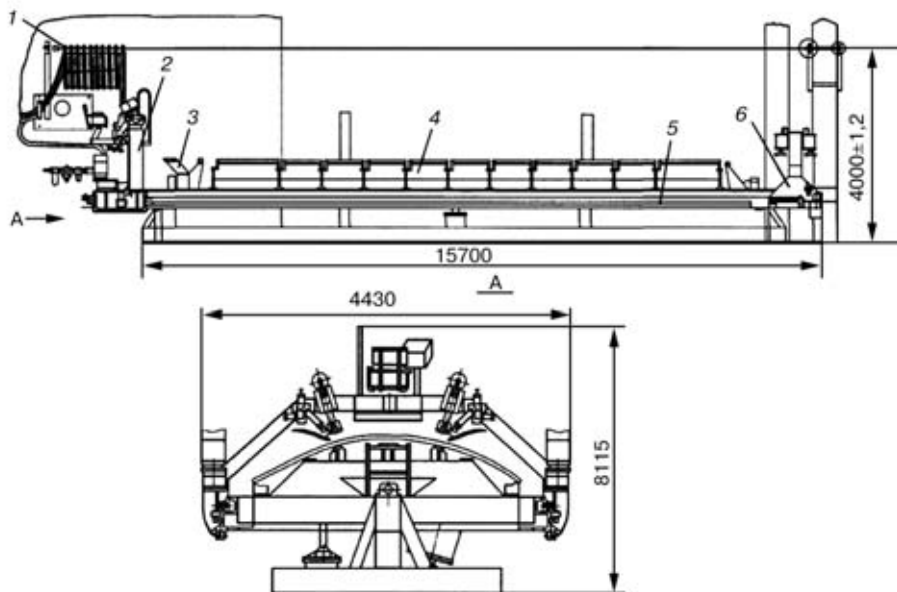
Установка сборки и автоматической сварки крыши цементовоза: 1 — подвеска для кабелей; 2 — портал сварочный; 3 — кронштейн; 4 — сборочный стенд; 5 — направляющие; 6 — портал сборочный
